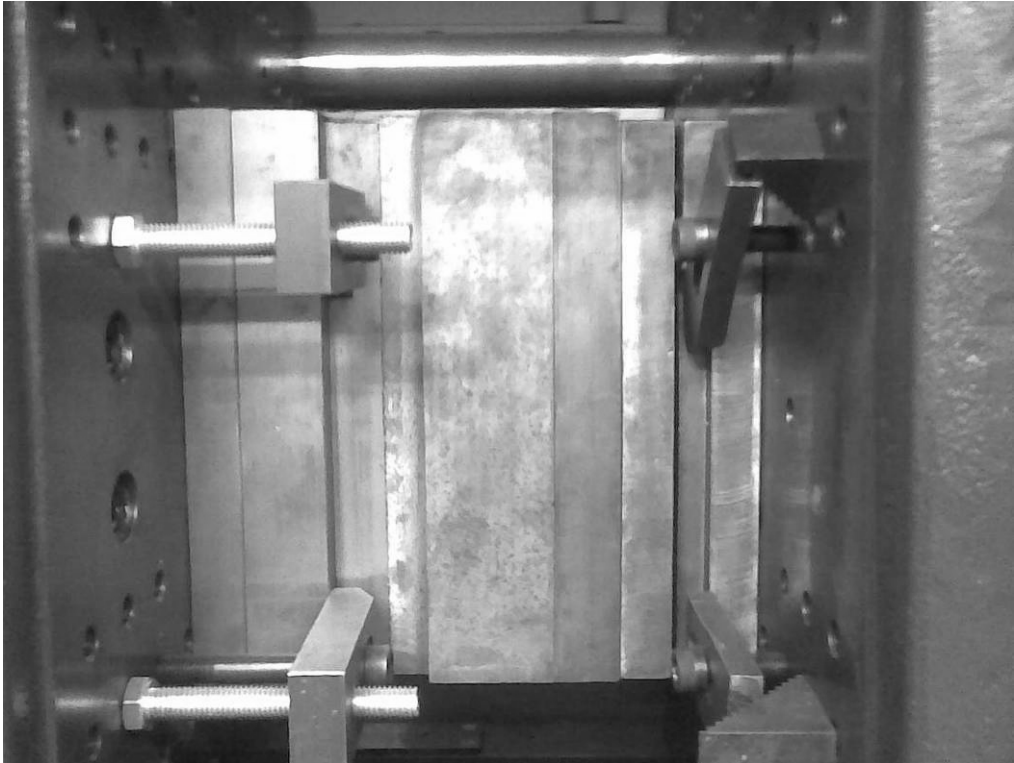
Vista frontal de las placas portamoldes, montadas en la máquina
